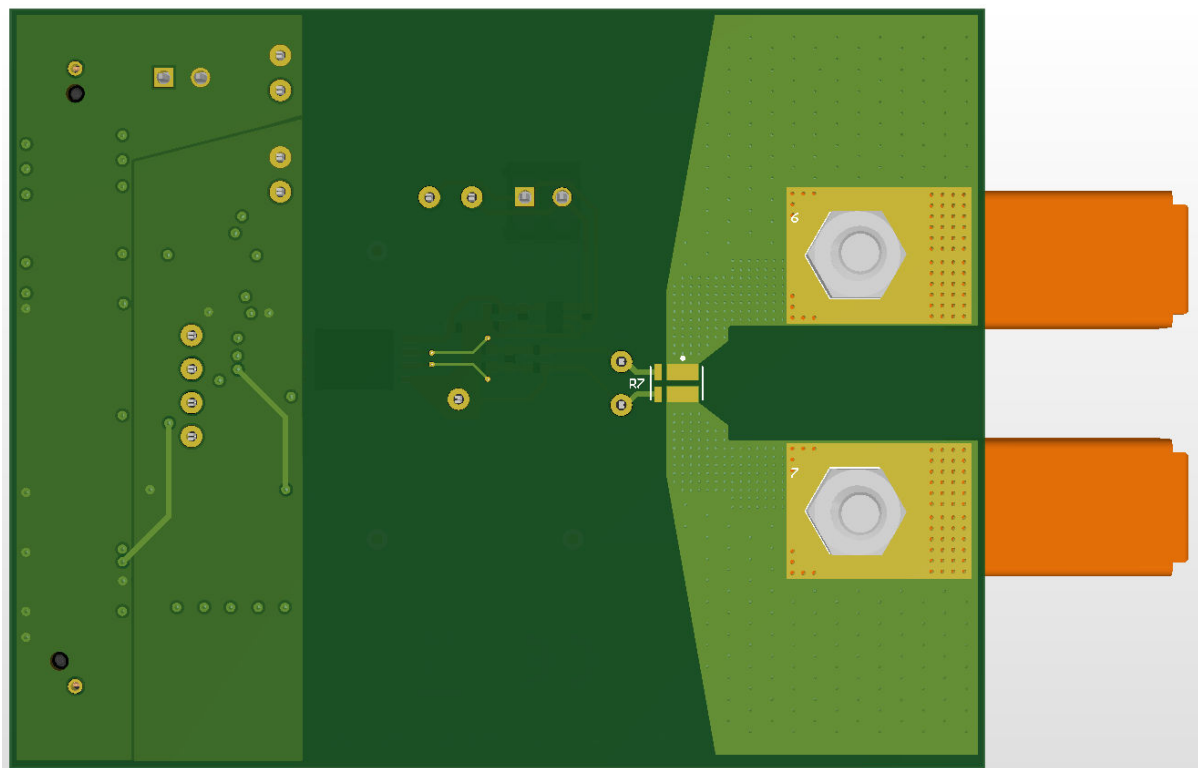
AMC-MOD-50A-EVM 底部 PCB 图
